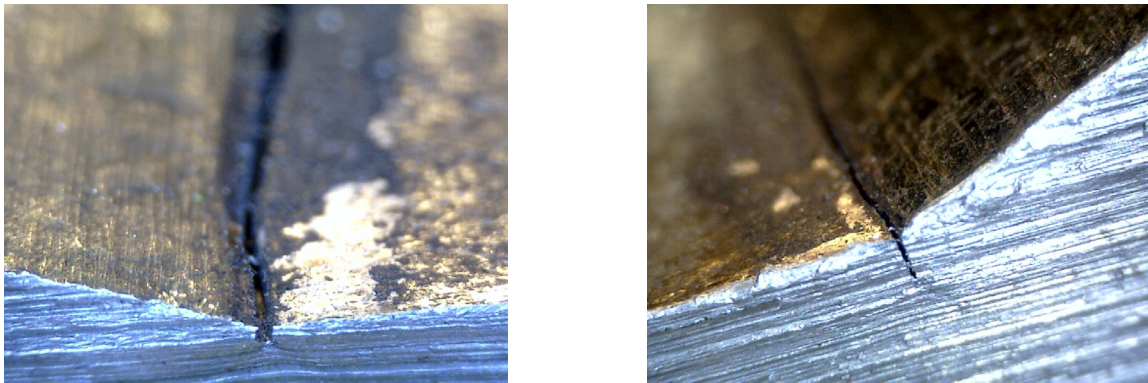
Exemplarische Aufnahmen durchgängiger Anrisse an der oberen Kerbe (Strichraupentechnik-Proben)
